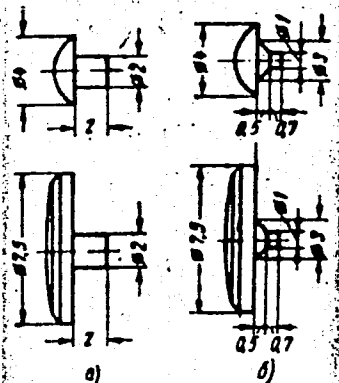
Серебряные контакты: а — для клепки; б — для точечной сварки.
